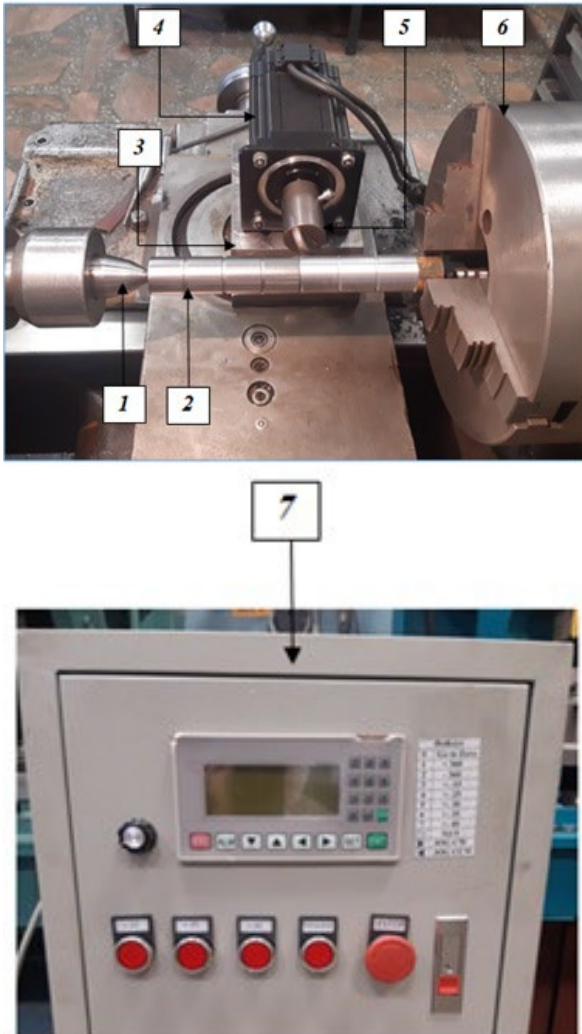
Общий вид устройства для реверсивного поверхностного пластического деформирования наружных поверхностей цилиндрических деталей на токарном станке:
